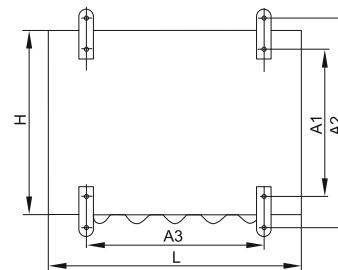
Вид корпуса сзади / Figure 1 – Enclosure back elevation / 1 сурет – Корпустың артқы көрінісі
